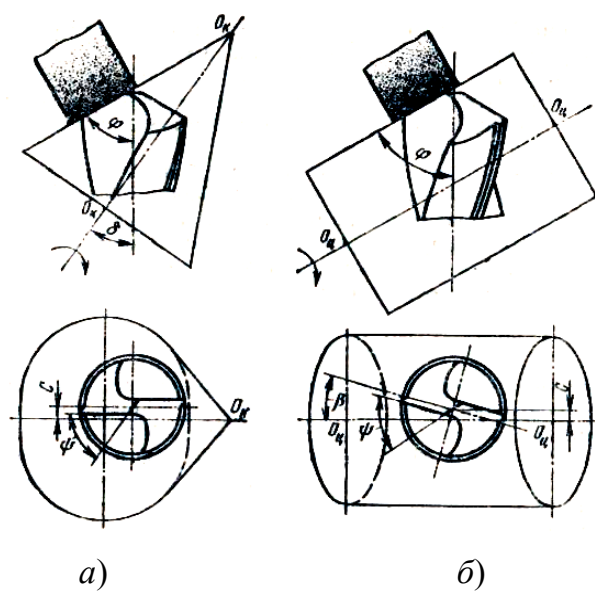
Схемы заточки сверла: коническая (а); цилиндрическая (б)
